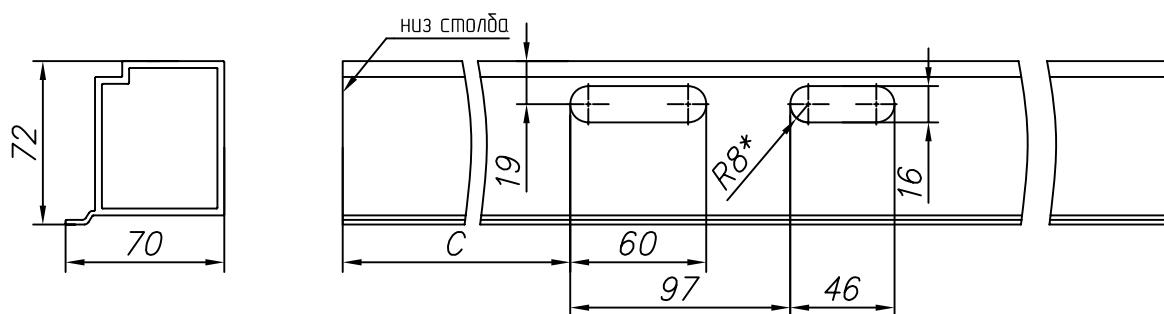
Изготовление столба притвора с пазом для ответной пластины замка для калитки с правым открыванием
